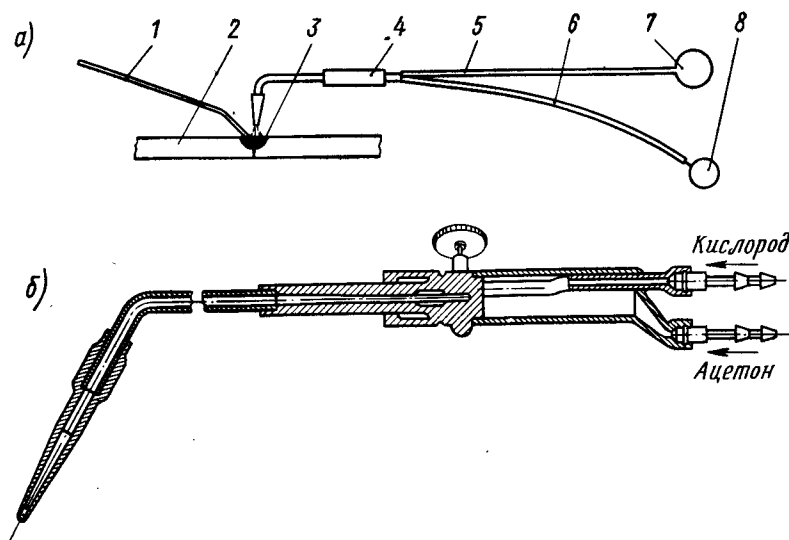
Схема газовой сварки металла (а) и сварочная горелка (б):
